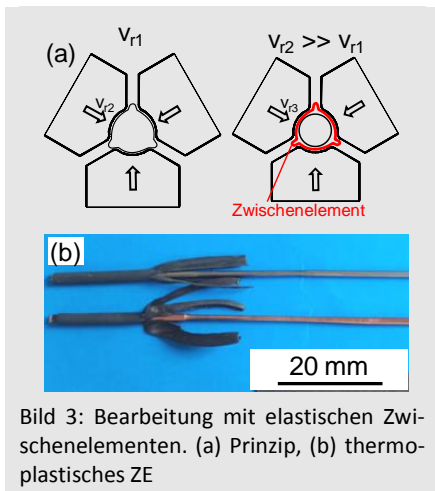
Bearbeitung mit elastischen Zwischenelementen. (a) Prinzip, (b) thermoplastisches ZE
